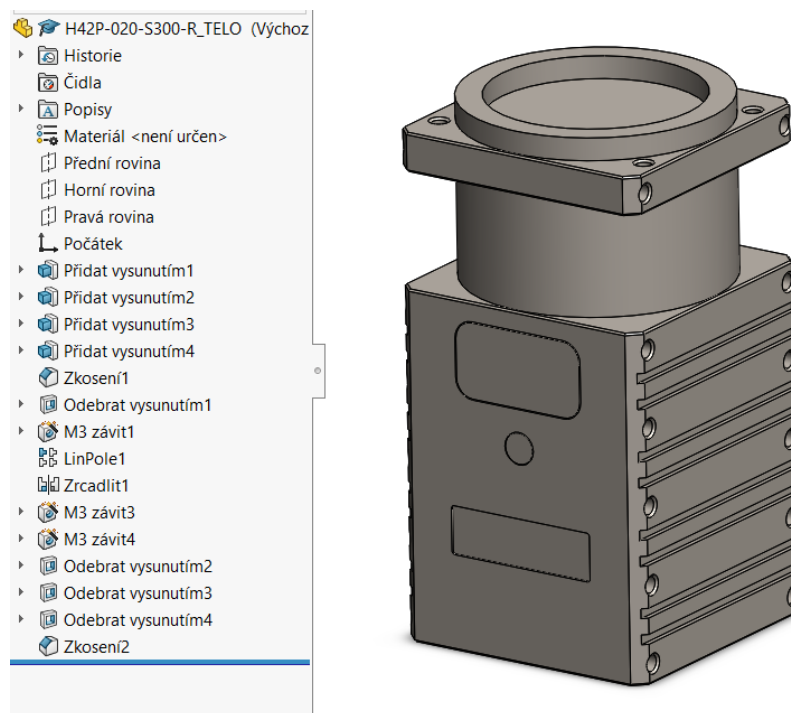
H42-P-020-S300-R\_telo – drážky a sražení
